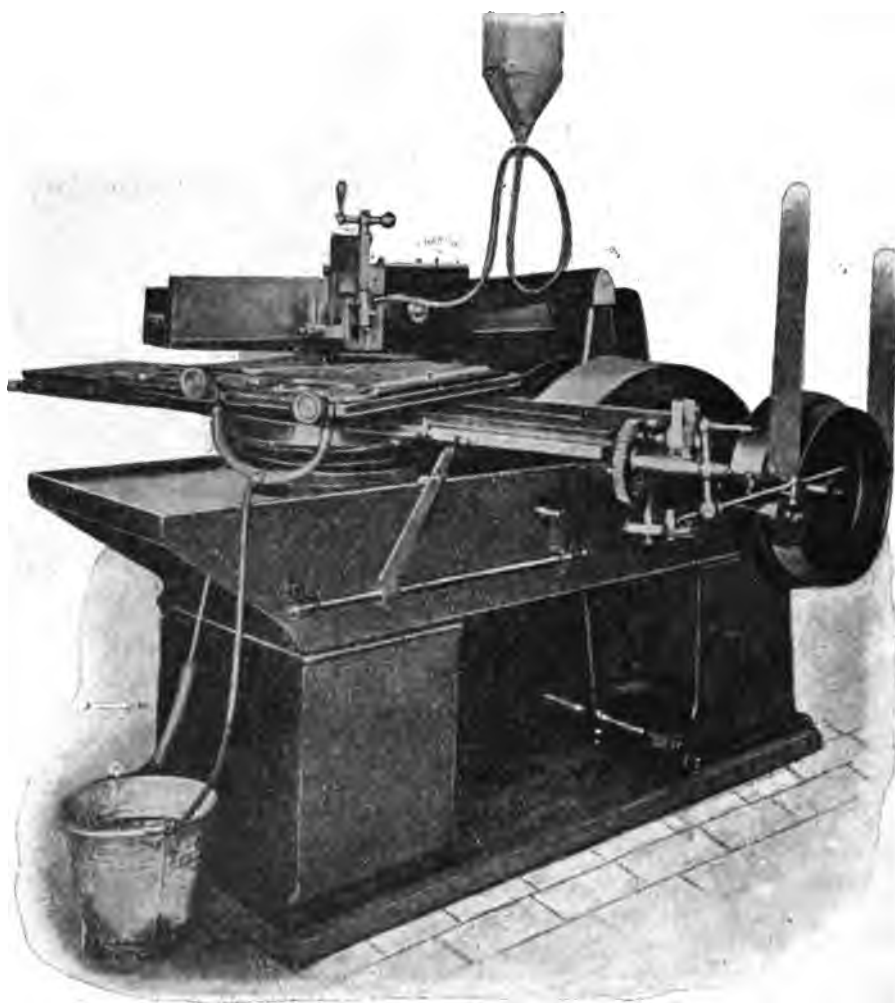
Machine Majert-Berg pour la fabrication des plaques.
